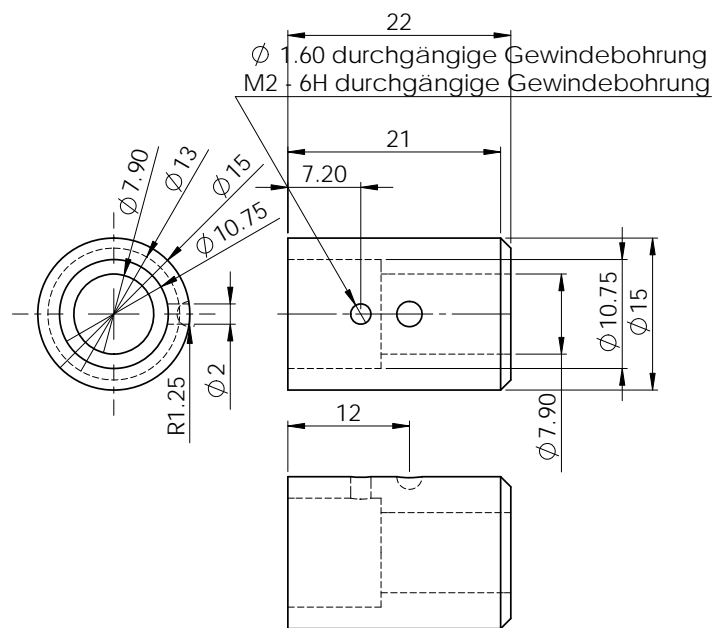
Technische Zeichnung des Zwischenrings der Beleuchtung.
